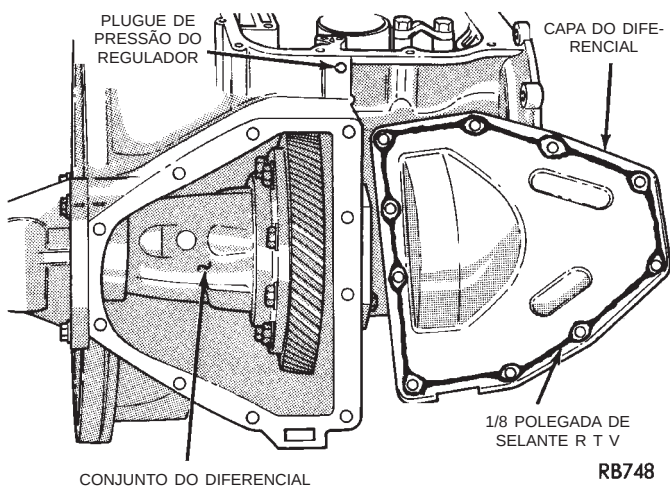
Remoção ou Instalação da Capa do Diferencial
